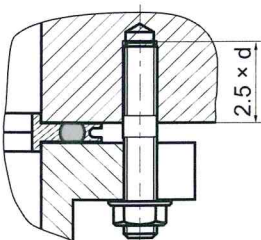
Flanschverbindung ISO-F, Stiftschraube und Gewindebohrung
